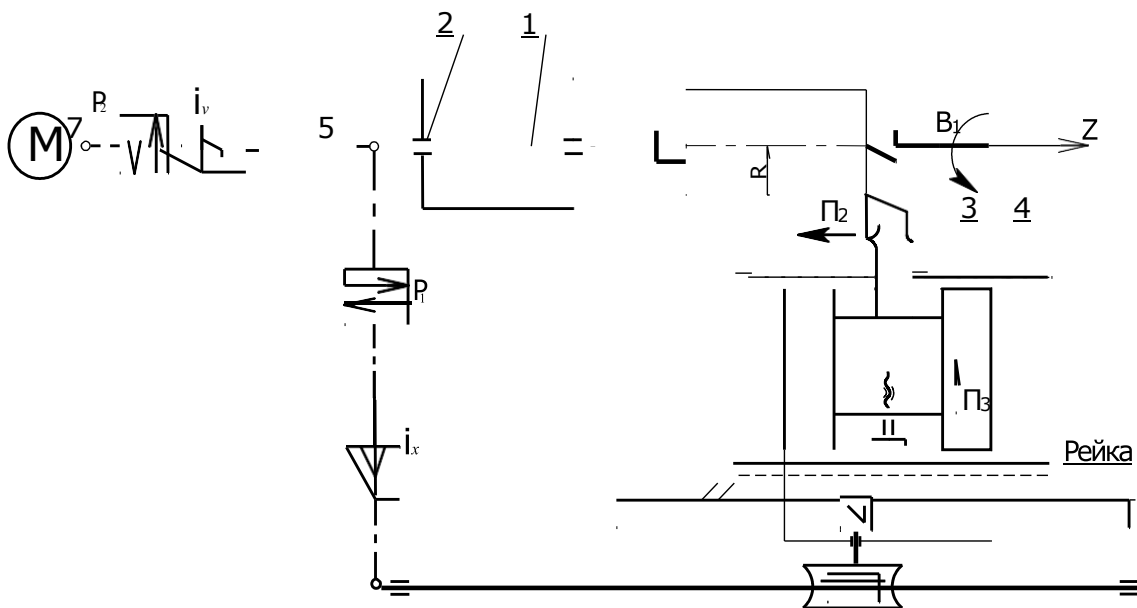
Кинематическая структура токарно-винторезного станка при точении
